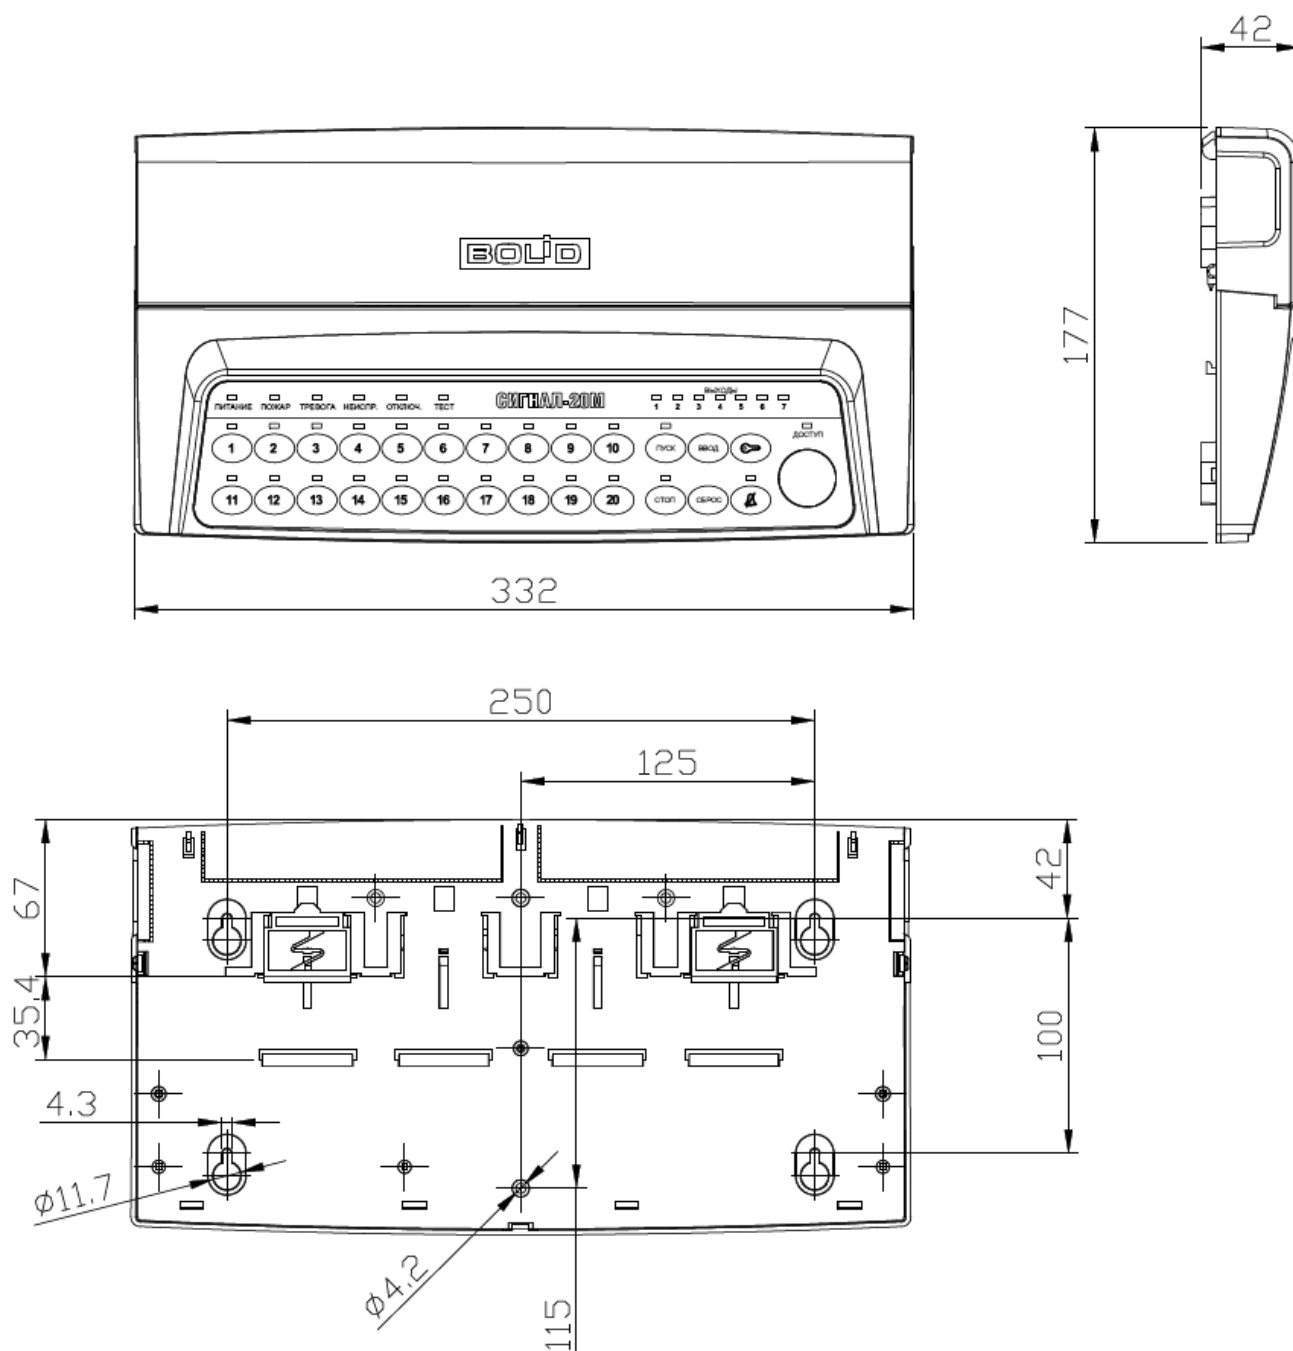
Внешний вид, габаритные и установочные размеры прибора
